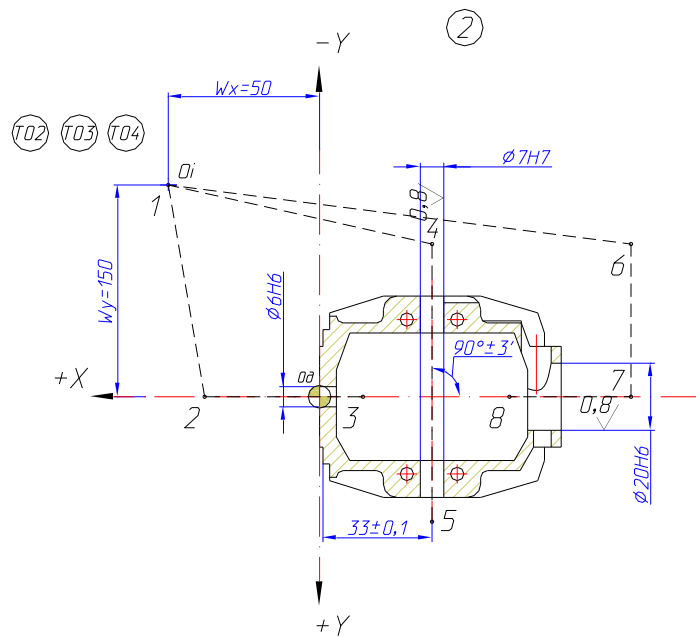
траєкторію зовнішнього контуру інструментом при обробленні деталі
